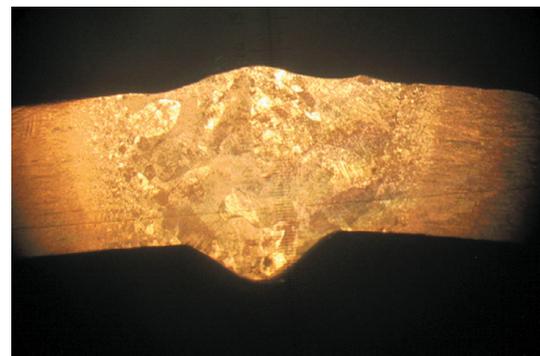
Внешний вид макрошлифа сварного шва
